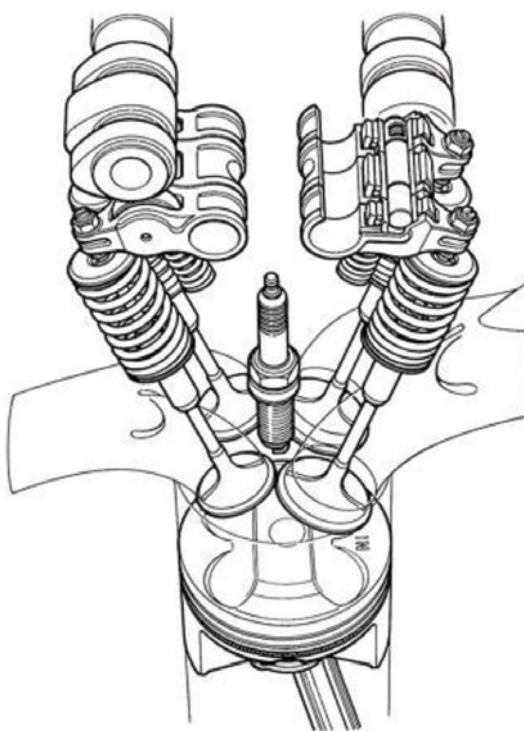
Механізм приводу клапанів газорозподілу VTEC
